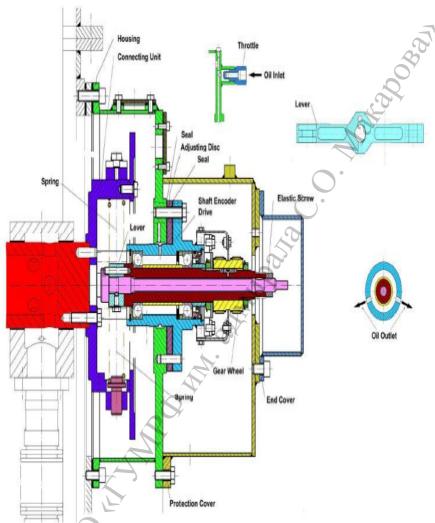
CA - sensor (CAS) — Датчик положения коленчатого вала: Housing - Крепление, Connecting unit - Модуль соединения, Spring - Пружина, Seal - Сальник, Adjasting Disc — «Смежный» диск, Shaft Encoder drive - Вал на «участке привода» декодера, Elastic Screw - Эластичный винт, Gear Wheel — «Приводная «передача, End Cover — Задняя крышка
